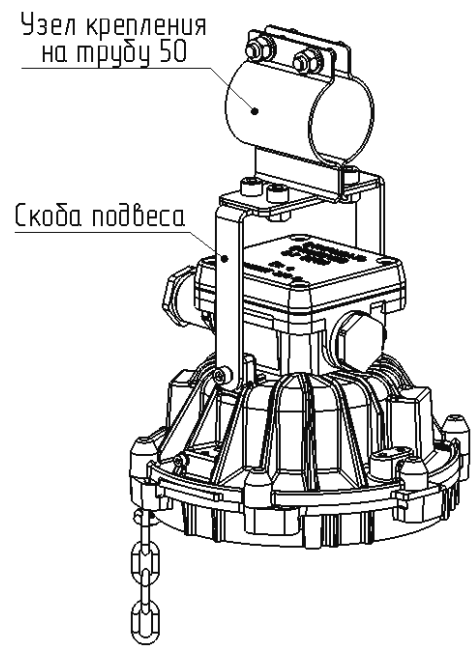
Светильник ДСП57КР-02, на узле крепления на трубу d=50мм.
